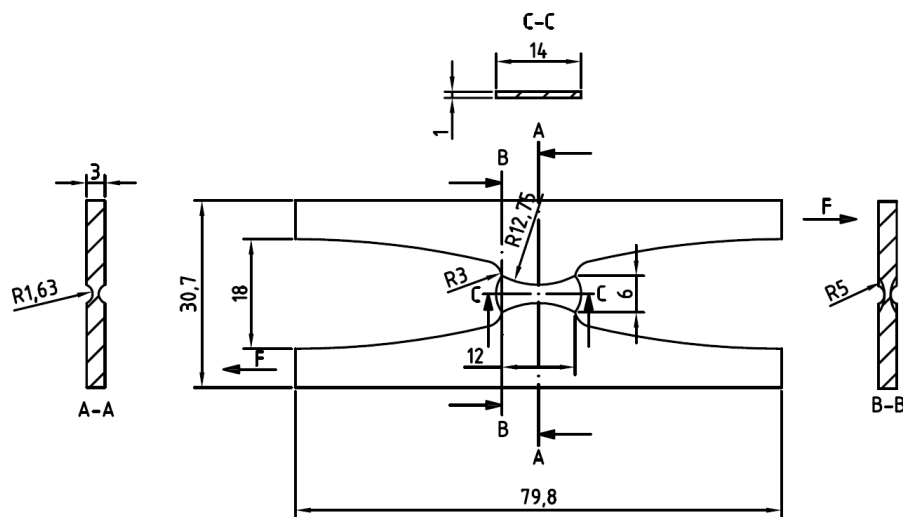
Geometria e direção de carregamento do provete borboleta sob solicitação de corte puro ($\alpha = 0^\circ$). Dimensões em mm.
